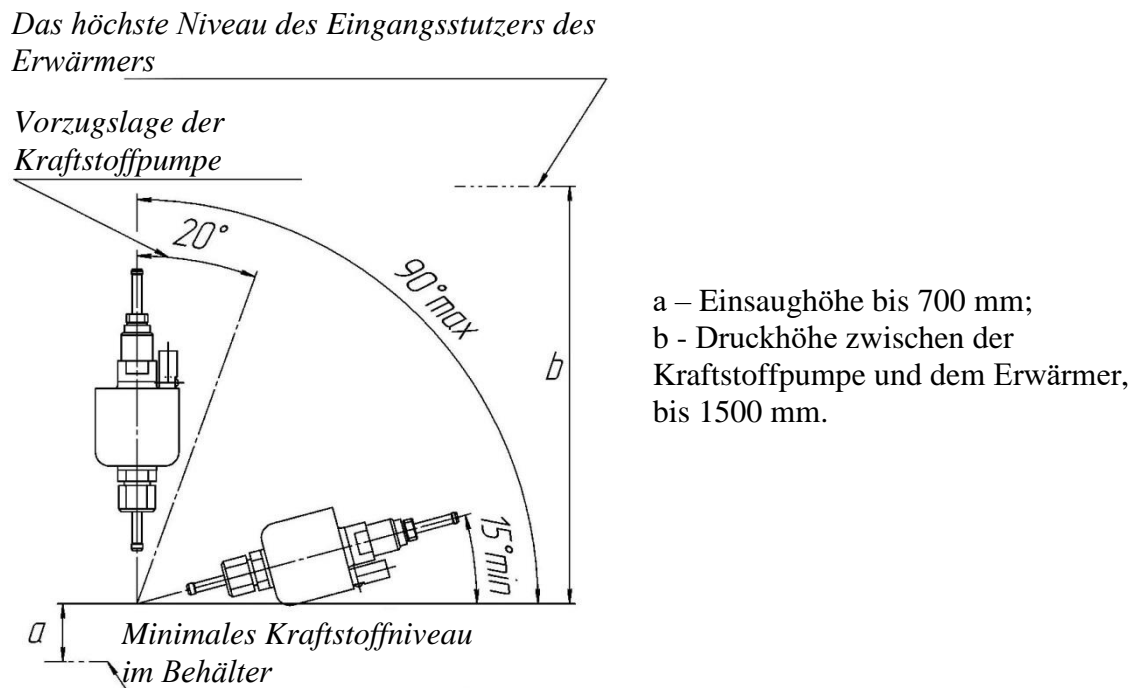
Zulässige Montagelage der Kraftstoffpumpe
